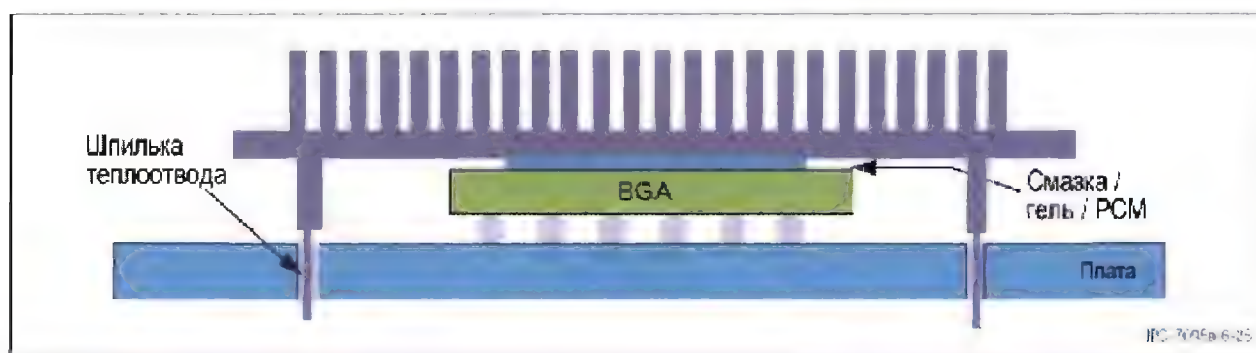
Радиатор, установленный на корпус BGA при помощи зажимов, крепящихся в отверстиях печатной платы
